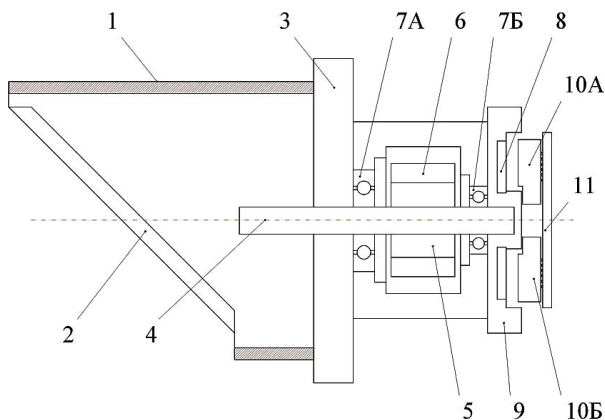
Конструкция привода отклоняющего устройства сканера FARO: 1 — держатель; 2 — отклоняющее зеркало; 3 — кольцевой диск; 4 — вал; 5 — ротор электродвигателя; 6 — статор электродвигателя; 7А, 7Б — пары подшипников; 8 — энкодер; 9 — корпус; 10А, 10Б — считывающие головки; 11 — печатная плата управления
